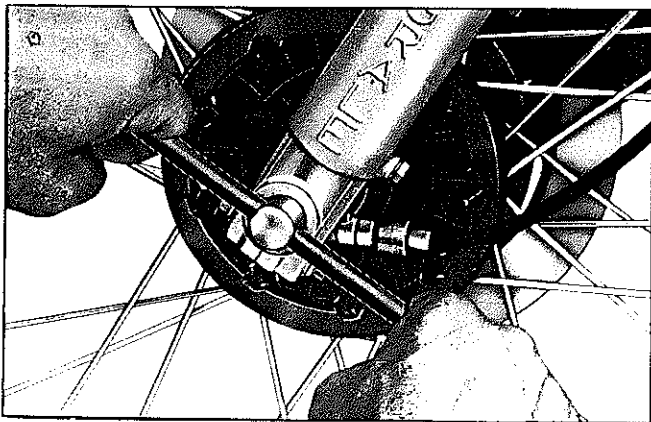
DESMONTAGEM DA RODA DIANTEIRA
